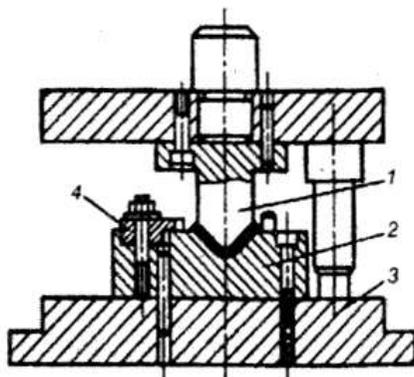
Схема штампа для гибки с регулируемым упором:
